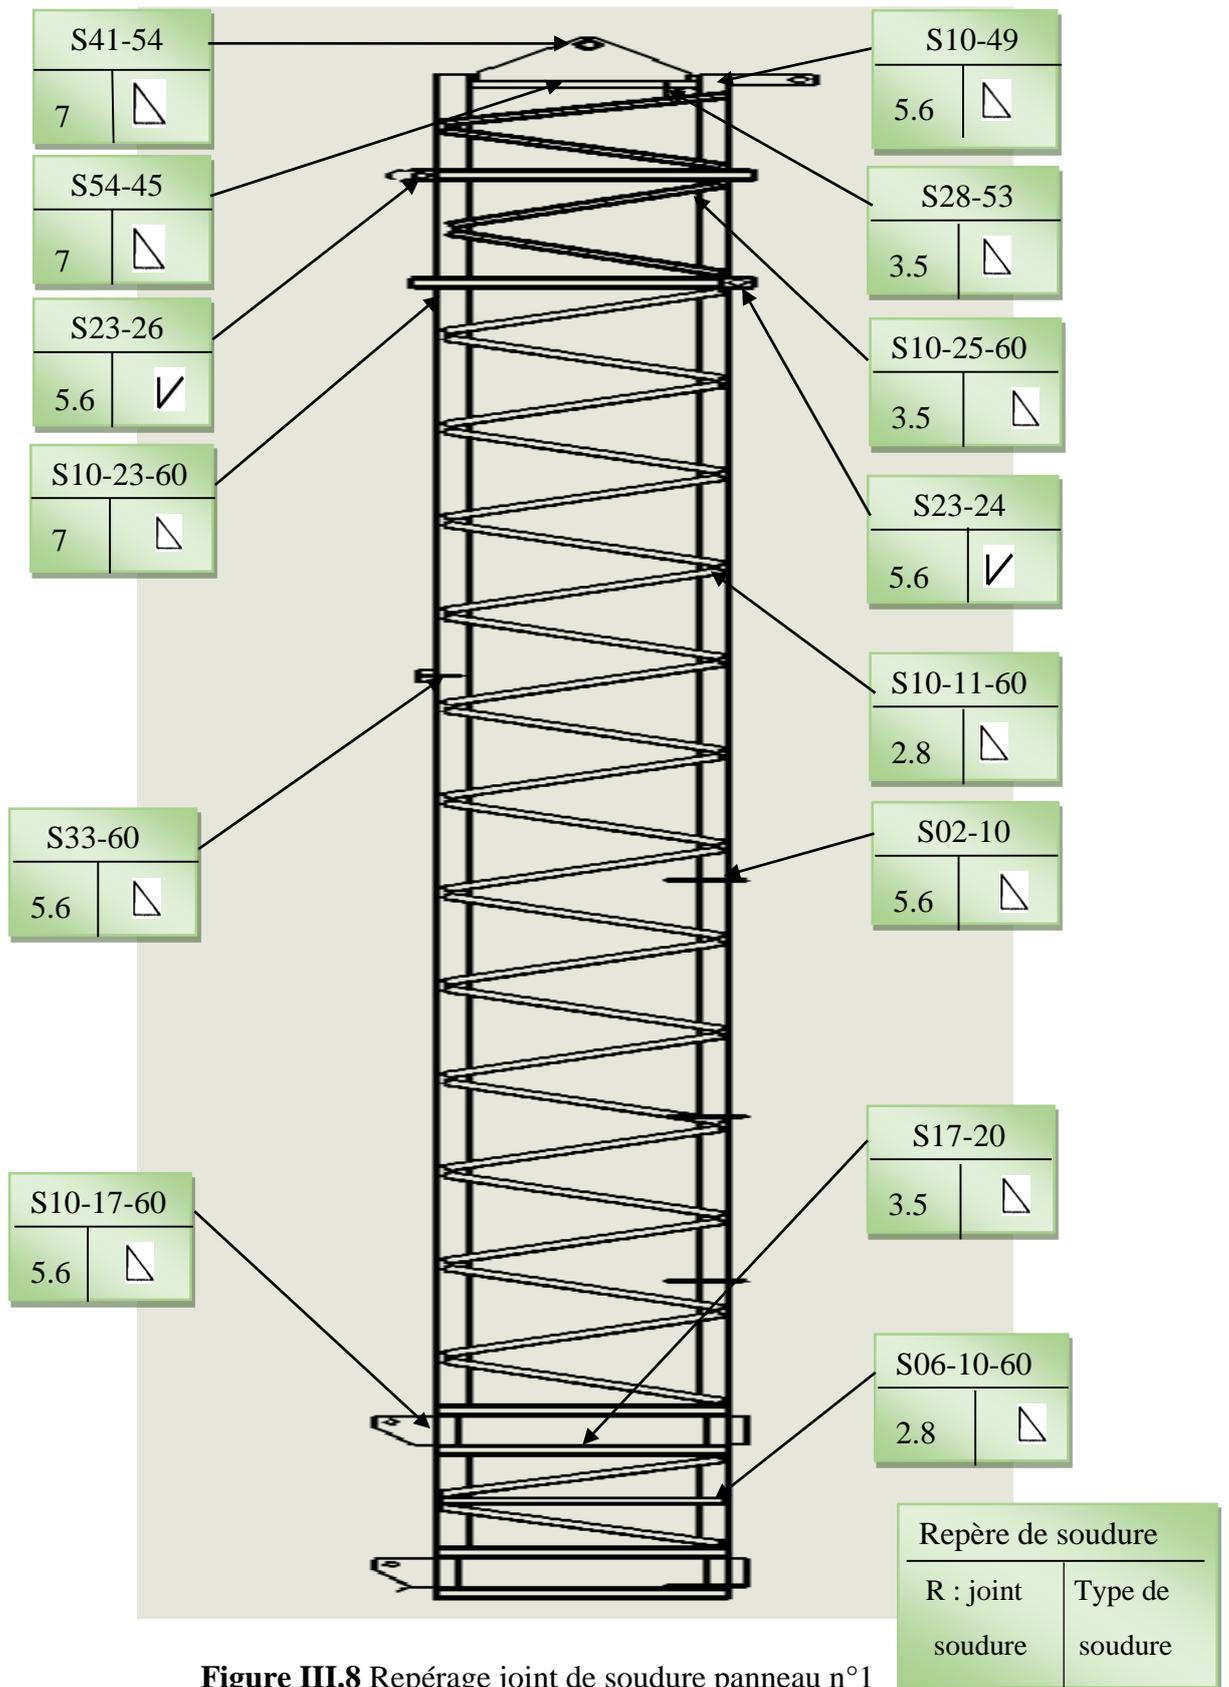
Repérage joint de soudure panneau n°1
